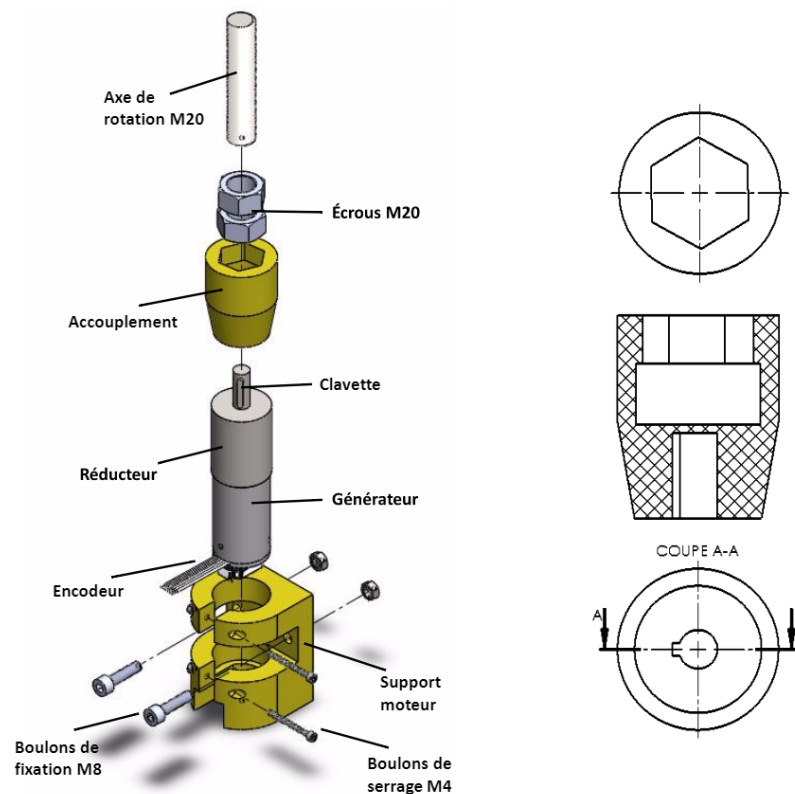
À gauche : vue éclatée de l'assemblage du générateur, à droite : coupe de la pièce d'accouplement imprimée en 3D
